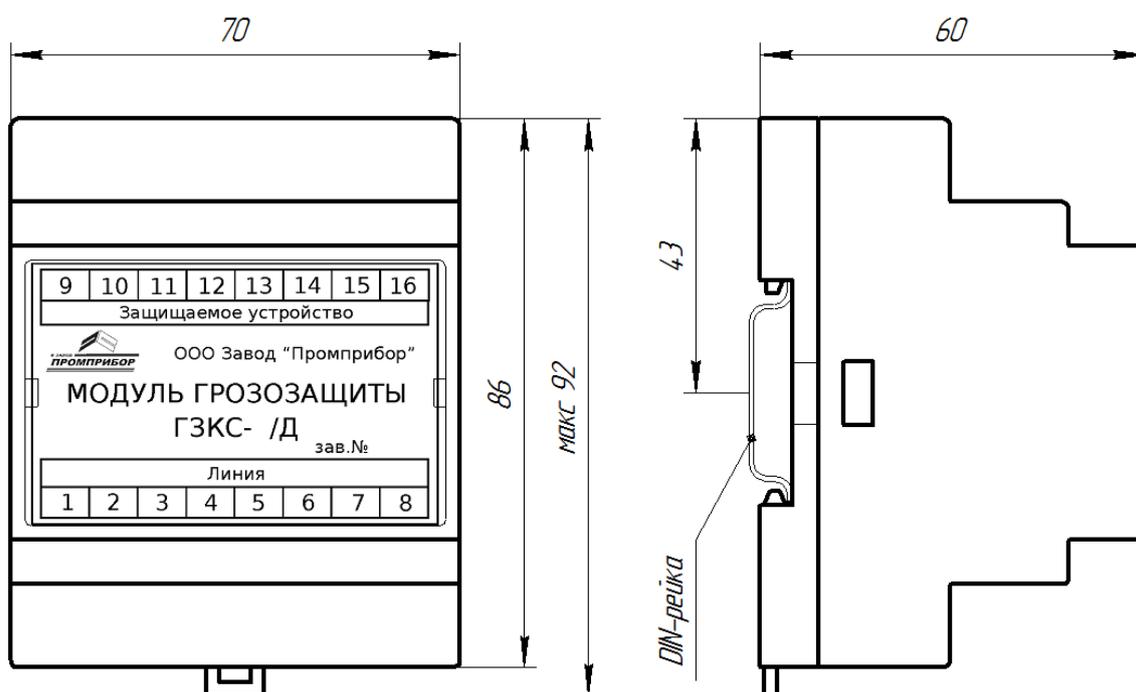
Габаритные и установочные размеры модуля грозозащиты
